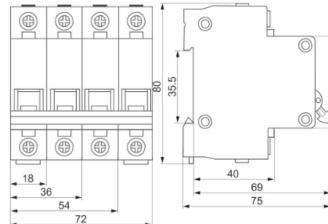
Габаритные, установочные, присоединительные размеры выключателей
